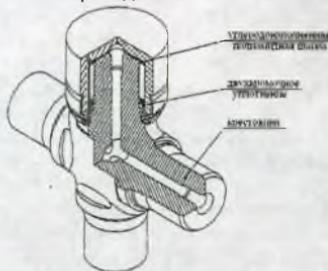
Крестовина в сборе с торцевым подшипником (в разрезе)
